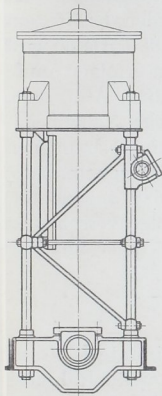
Rahmen für leichte Schiffsmaschinen.
